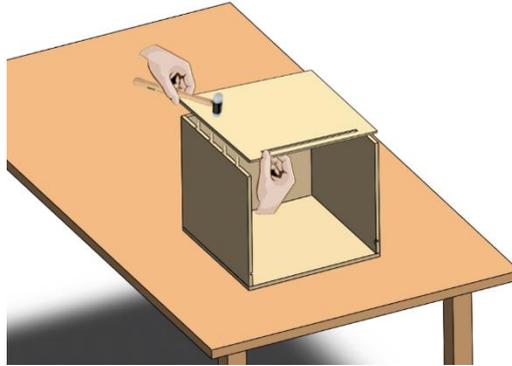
Paso 12 del ensamblaje del cajón (conjunto 2)
